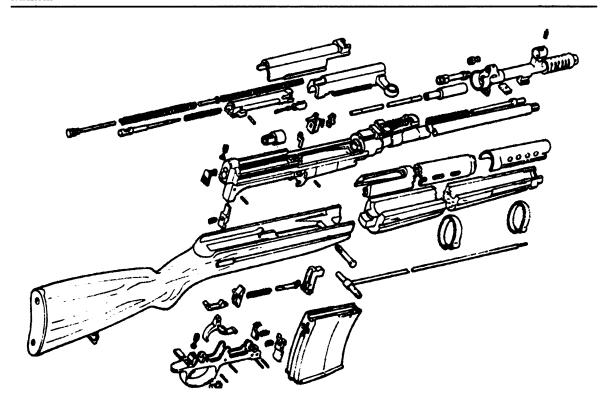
Вид деталей и узлов винтовки СВТ-38
